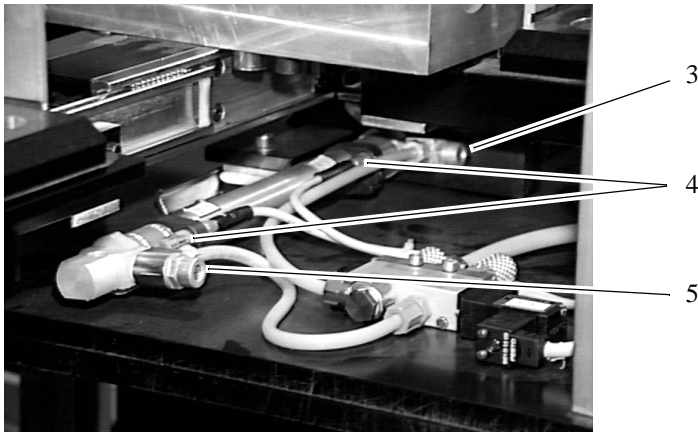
Pneumatik-Zylinder, Ventil und Drosseln
